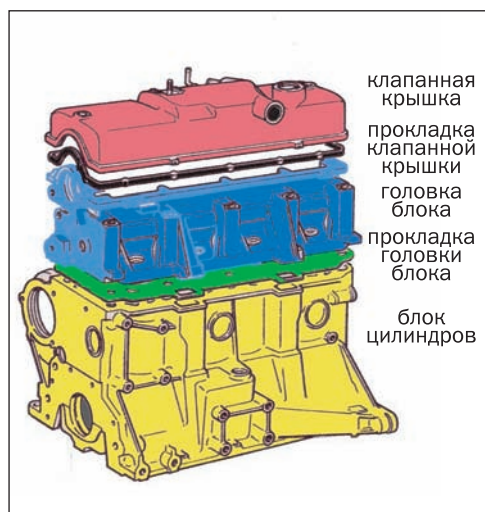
Неподвижные детали кривошипно-шатунного механизма
